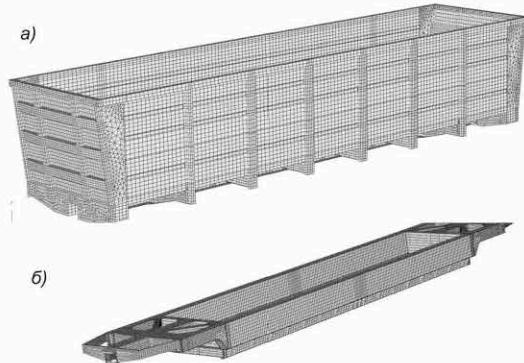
Конечно-элементные модели металлоконструкций кузовов вагонов:
